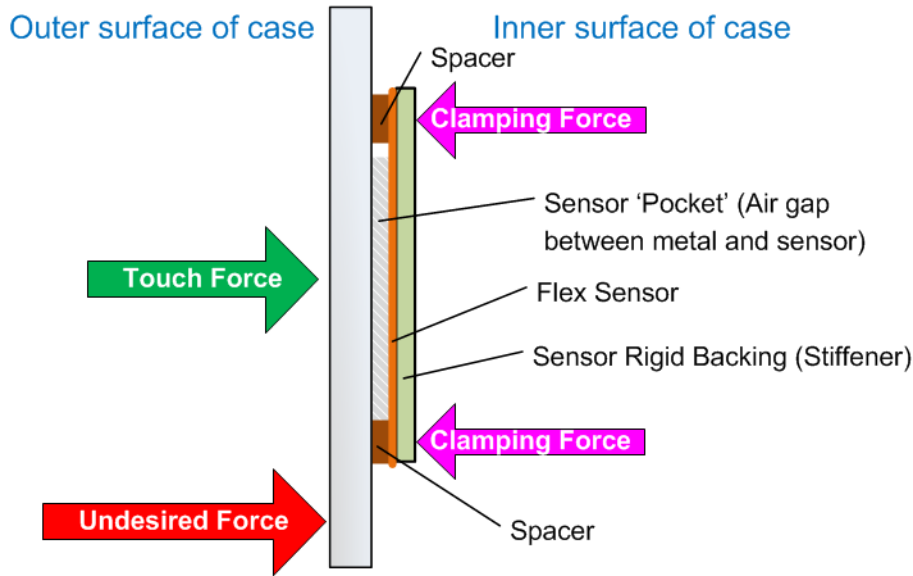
具有金属目标和 PCB 传感器的按钮结构
